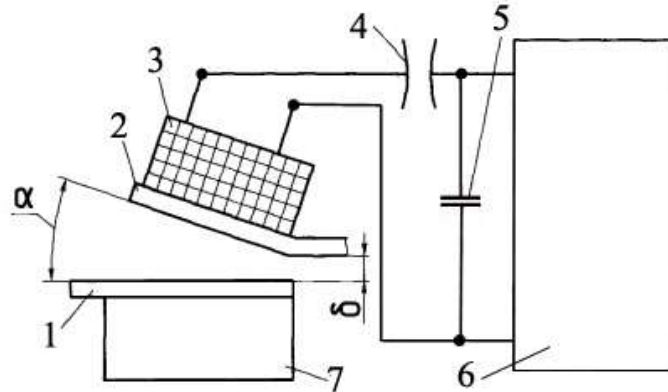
Схема магнітно-імпульсного зварювання:
